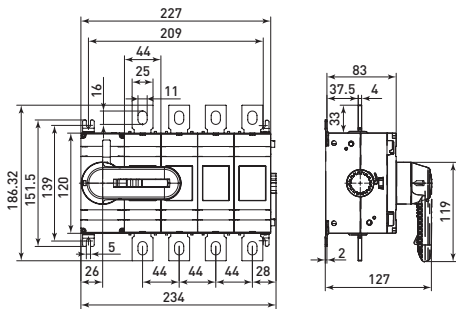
Габаритные и установочные размеры рубильников 315-400А 4Р
